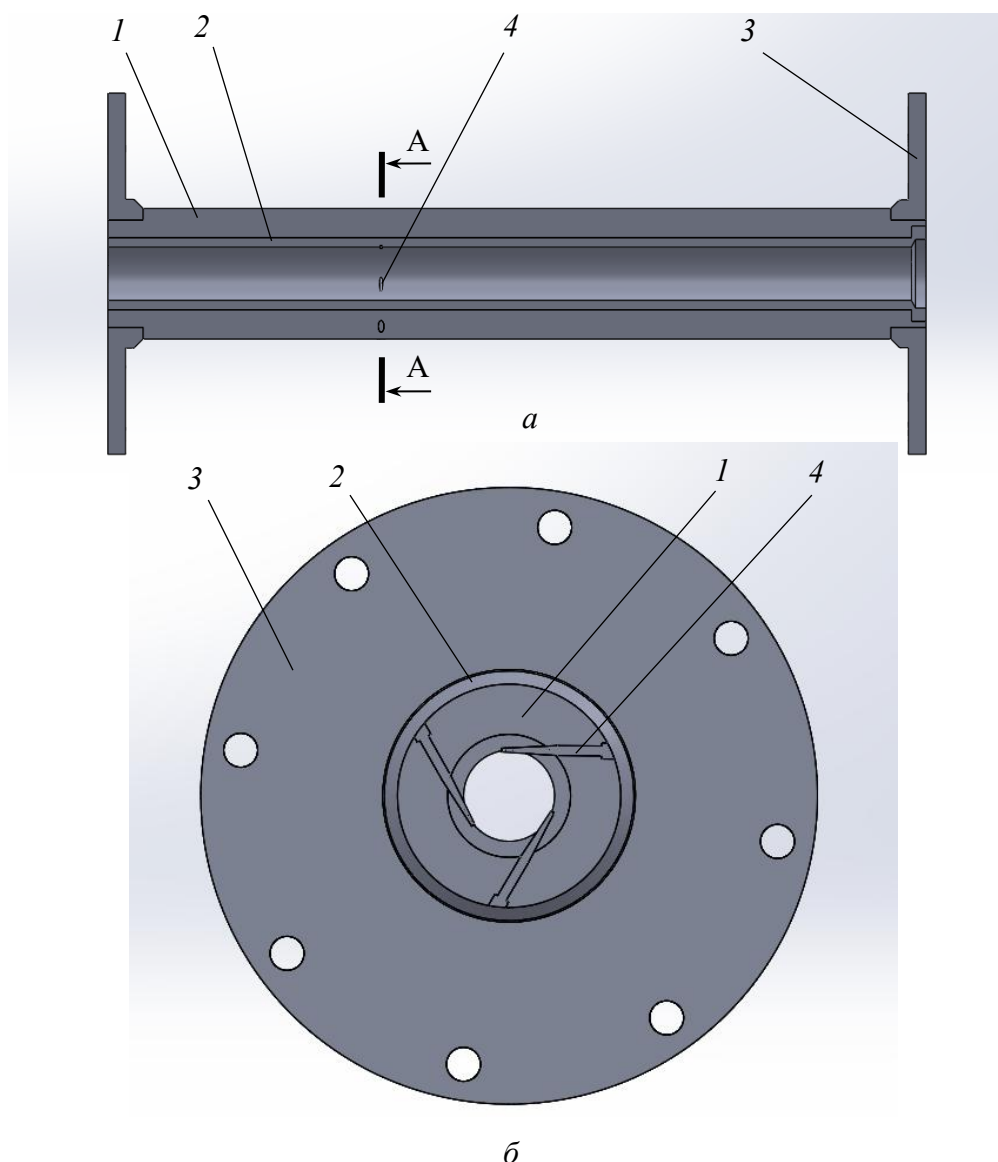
Модернізований корпус: *а* – вид збоку; *б* – поперечний розріз А-А (по місцю розташування штифтів): 1 – корпус, 2 – гільза, 3 – фланці, 4 – штифти
